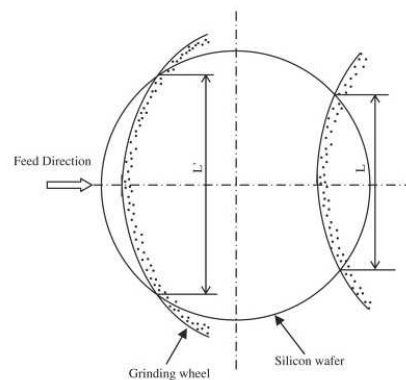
Surface de contact entre une meule et un wafer dans un grinder type Blanchard[22]
